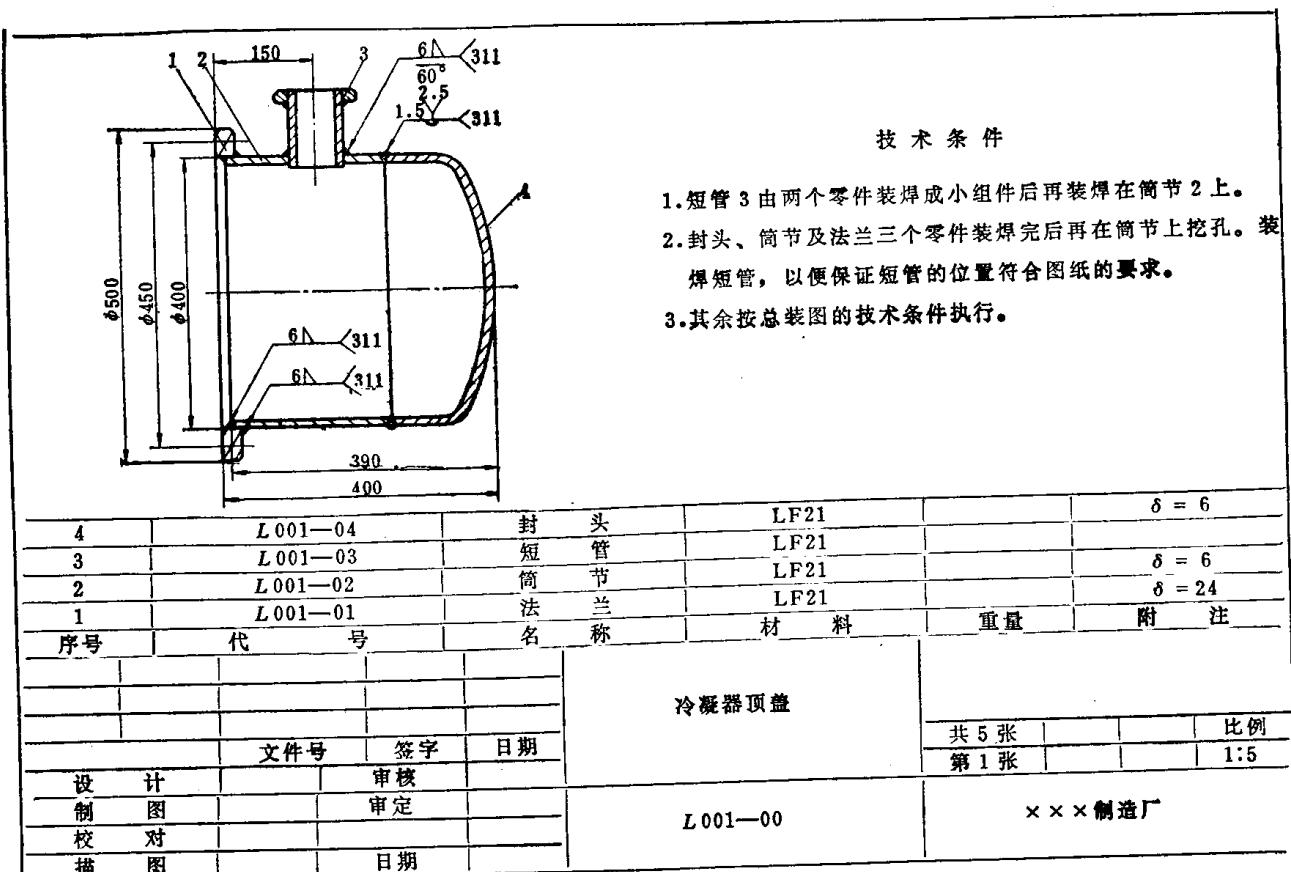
铝制冷凝器顶盖焊接装配图
